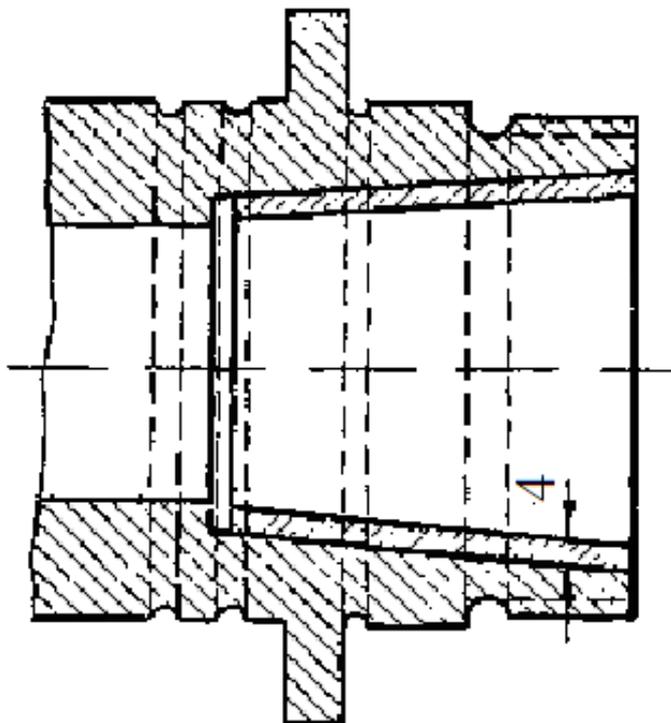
Схема восстановления конусного отверстия шпинделя запрессовкой или постановкой на эпоксидном клее втулки
